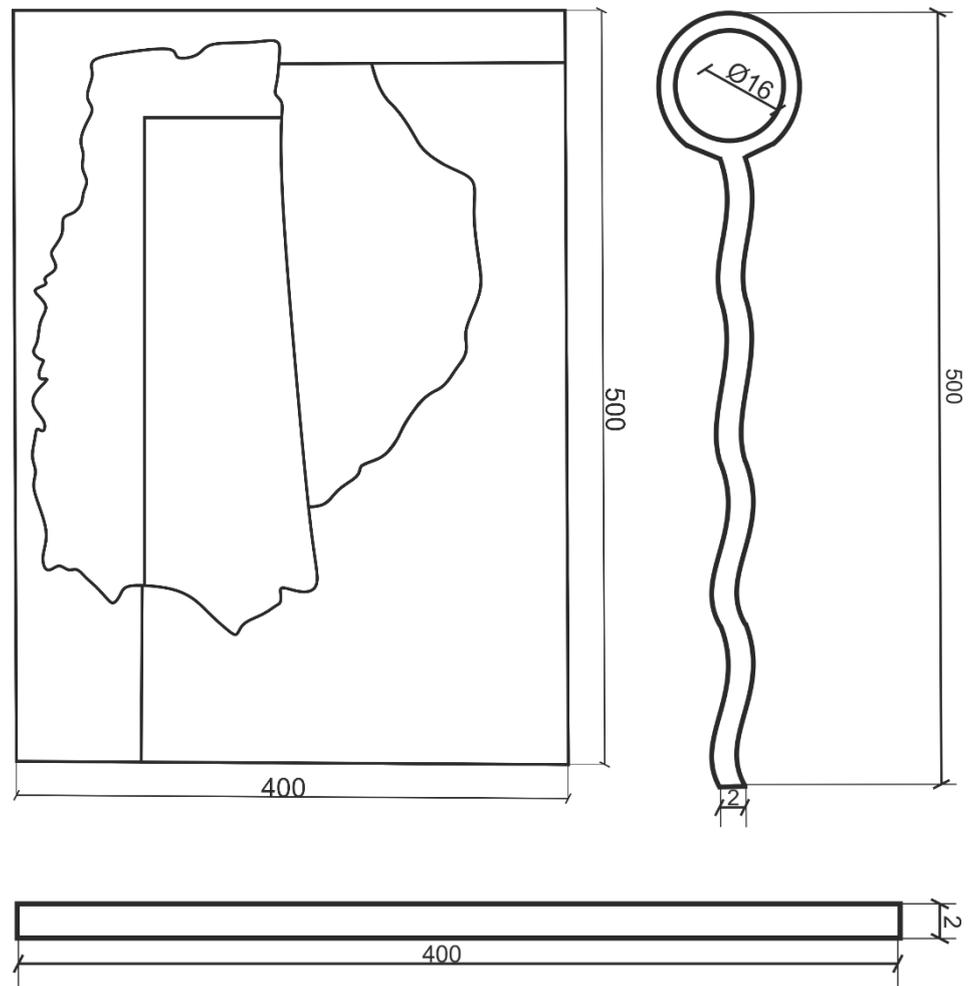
Mapa de daños. Alzado, perfil y planta de la pieza 2.
